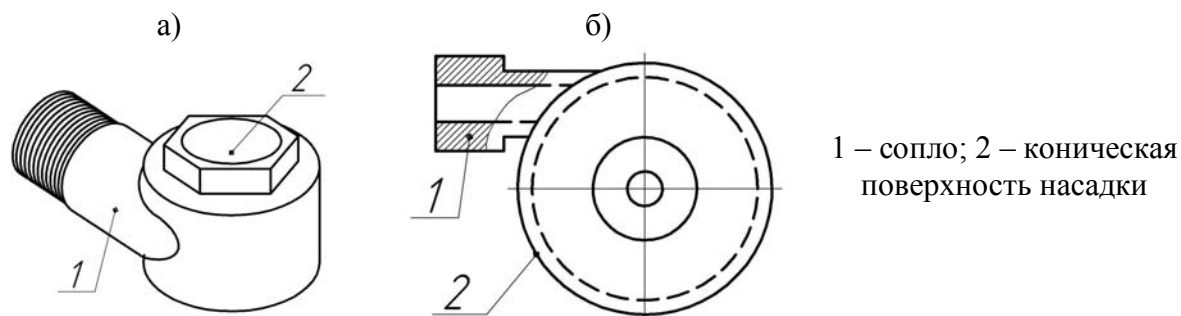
Общий вид (а) и конструктивная схема (б) центробежной насадки
